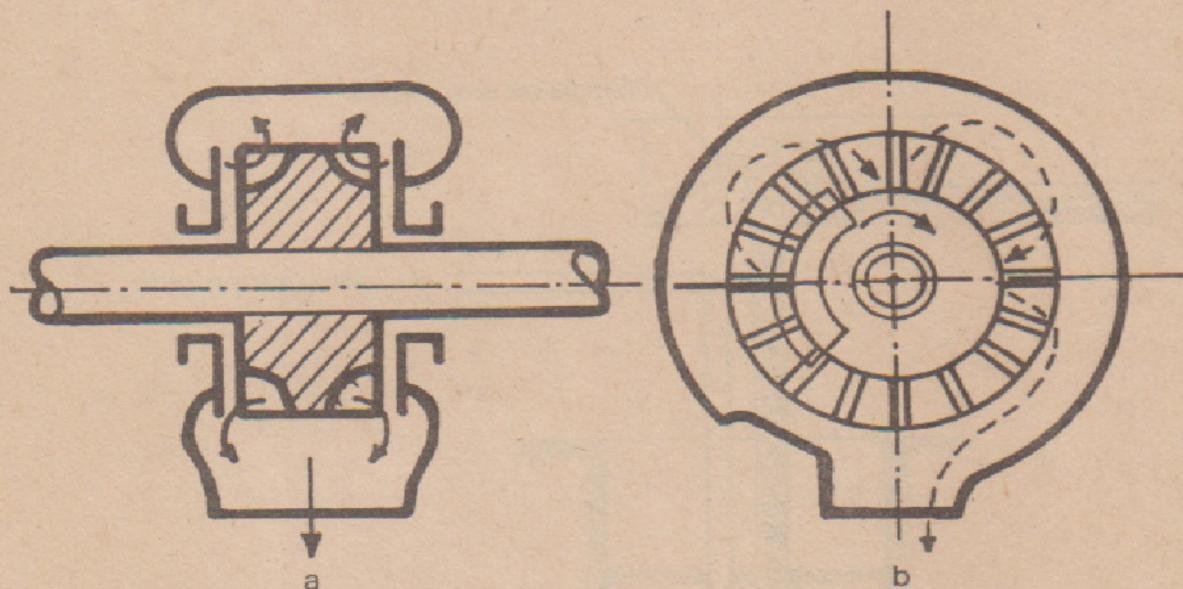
Esquema de una bomba de torbellino: a) corte transversal; b) vista lateral
